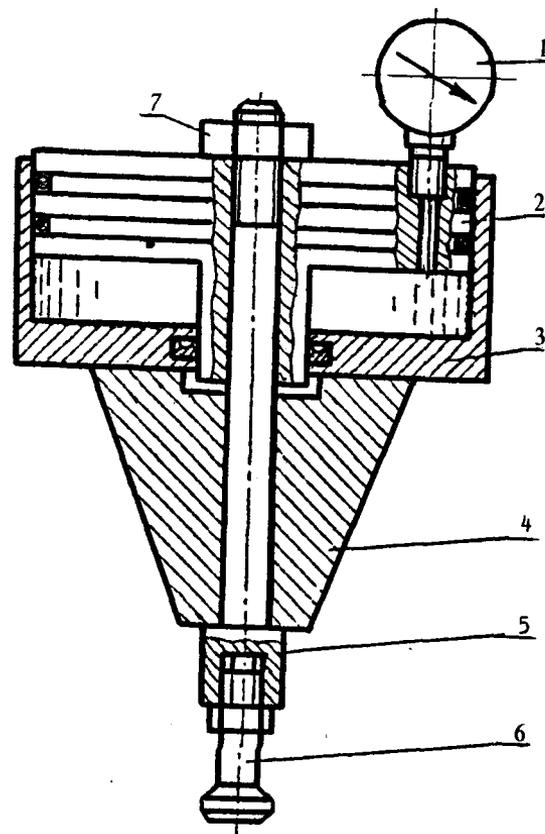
Динамометрическое устройство приспособления для контроля тарельчатых пружин:
